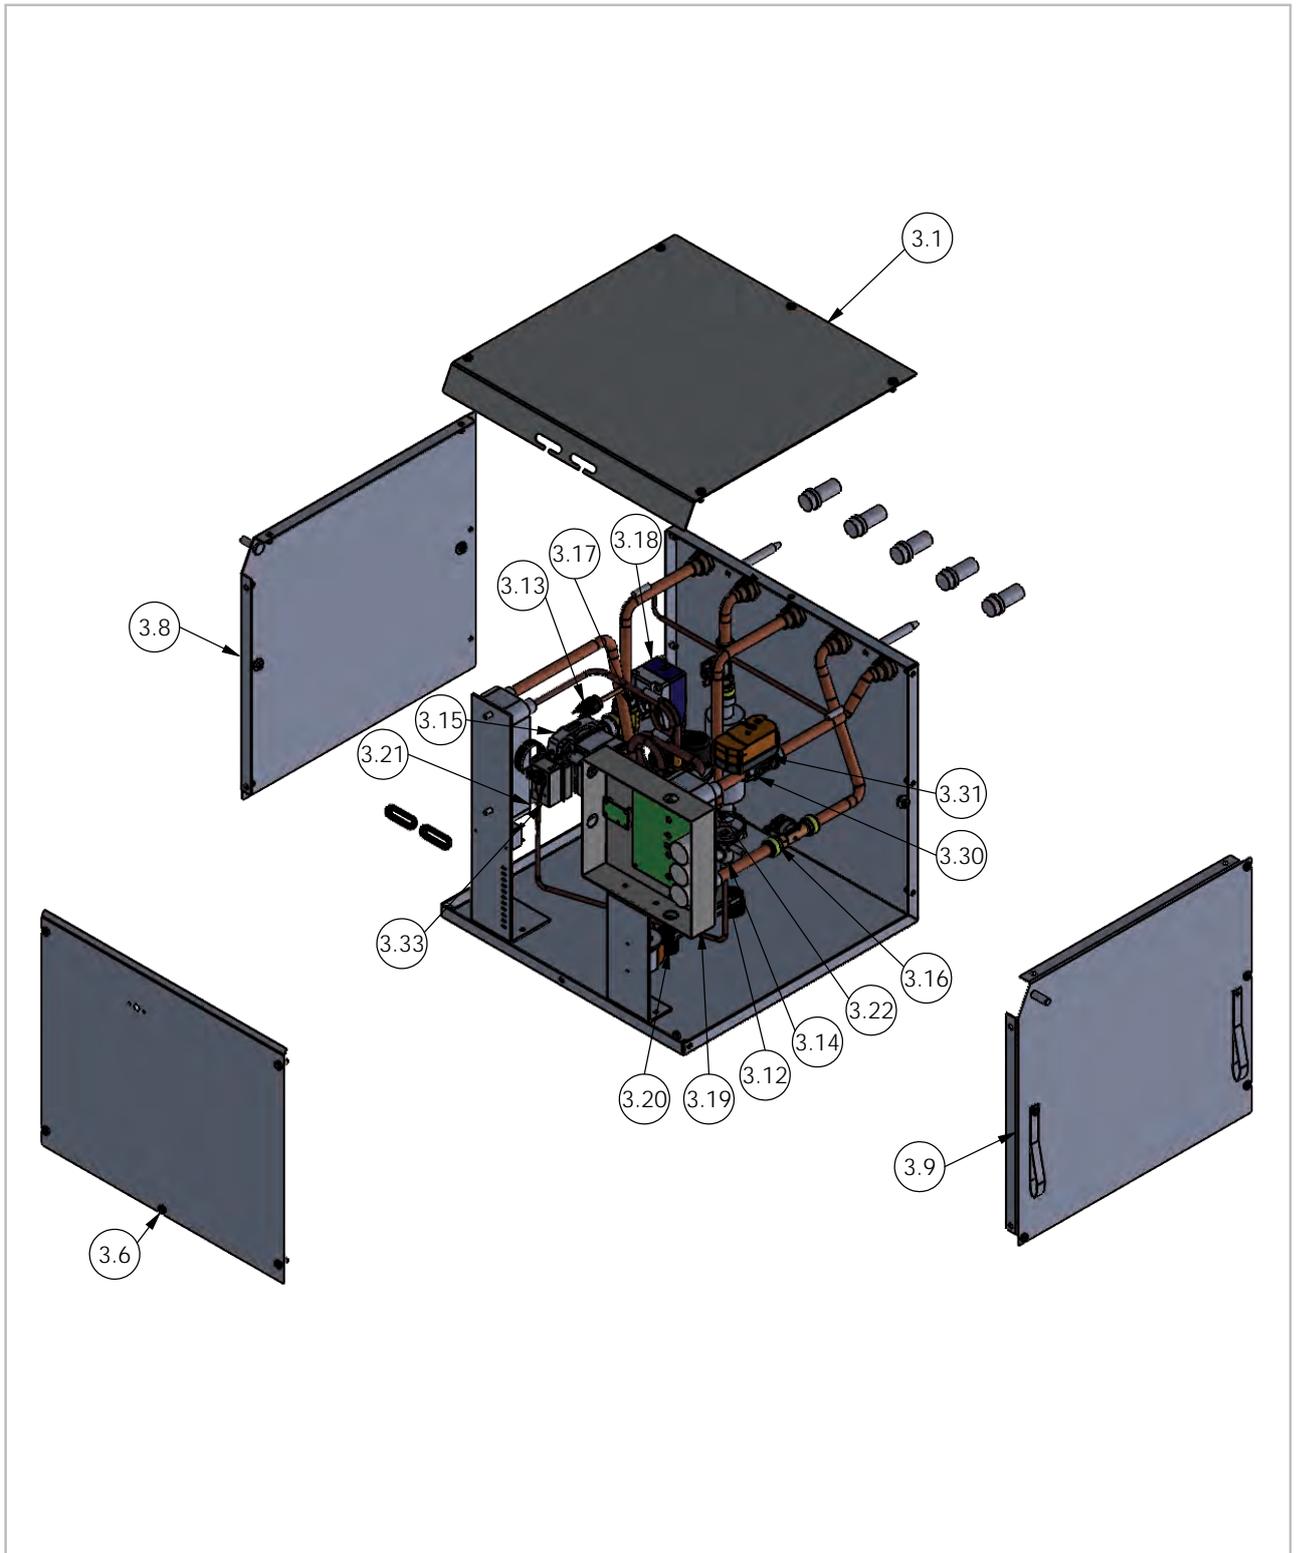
Explosionszeichnung Wärmepumpenmodul MWP 35
